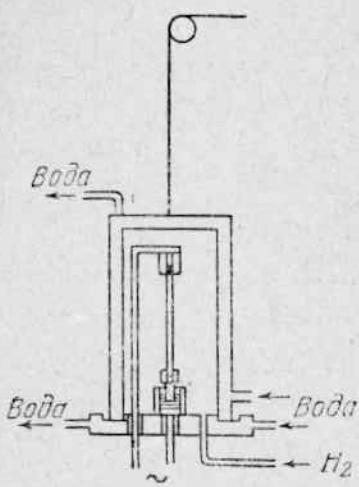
Схема аппарата для сварки вольфрамовых штабиков.
